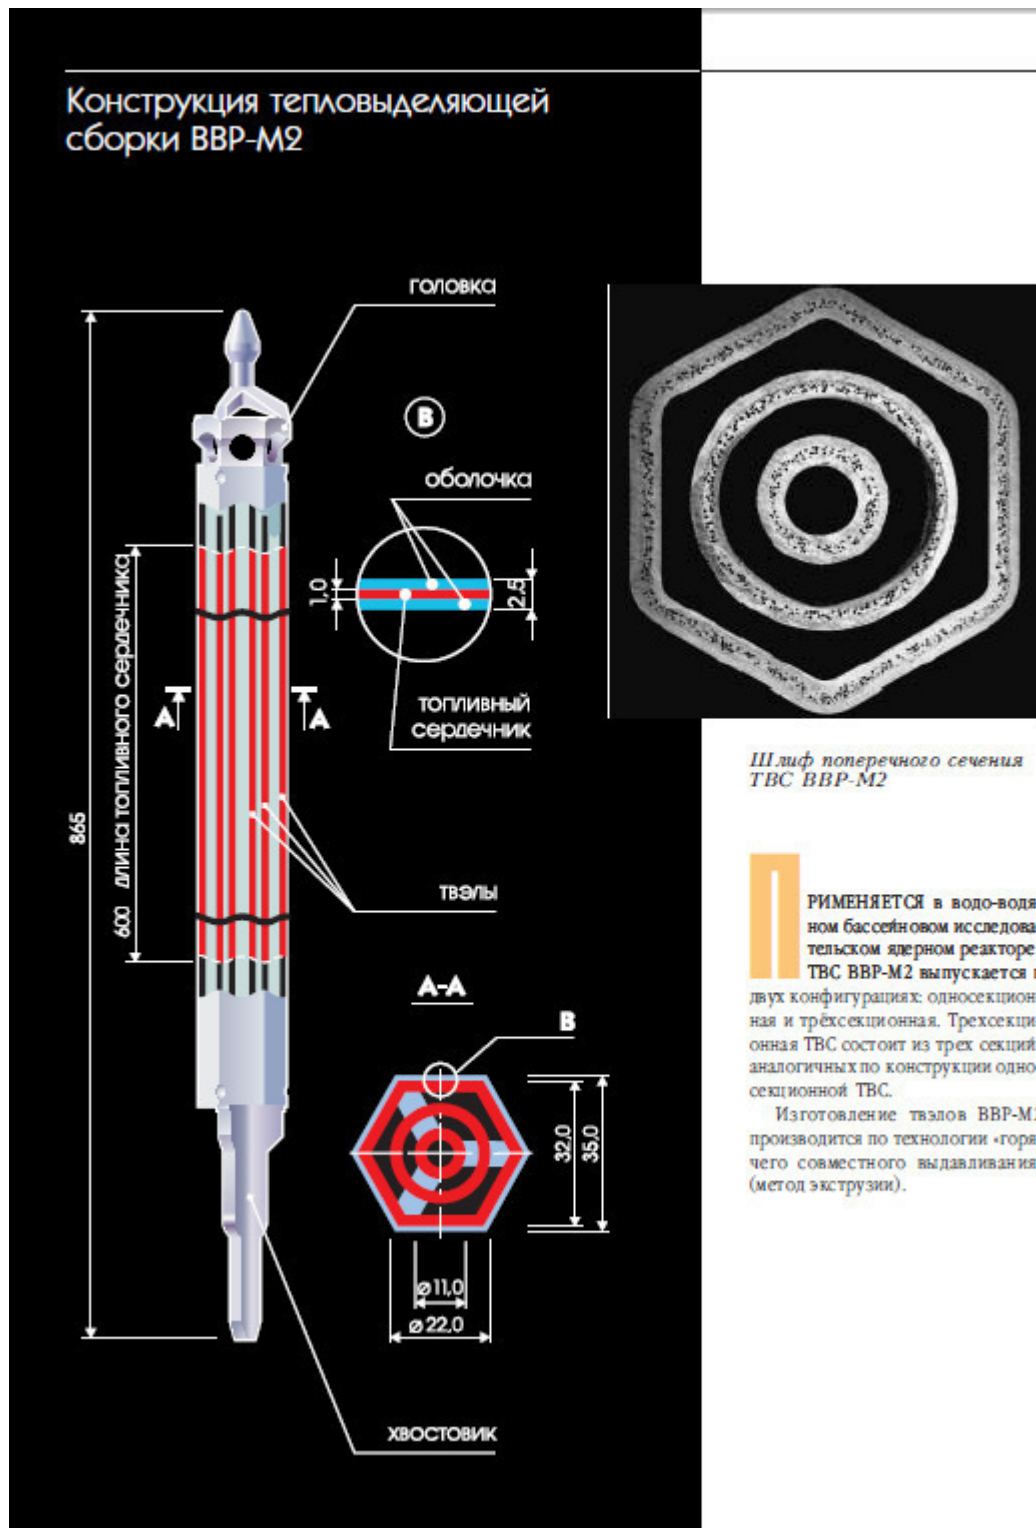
Общий вид ТВС и твэла реактора ВВР-М2
